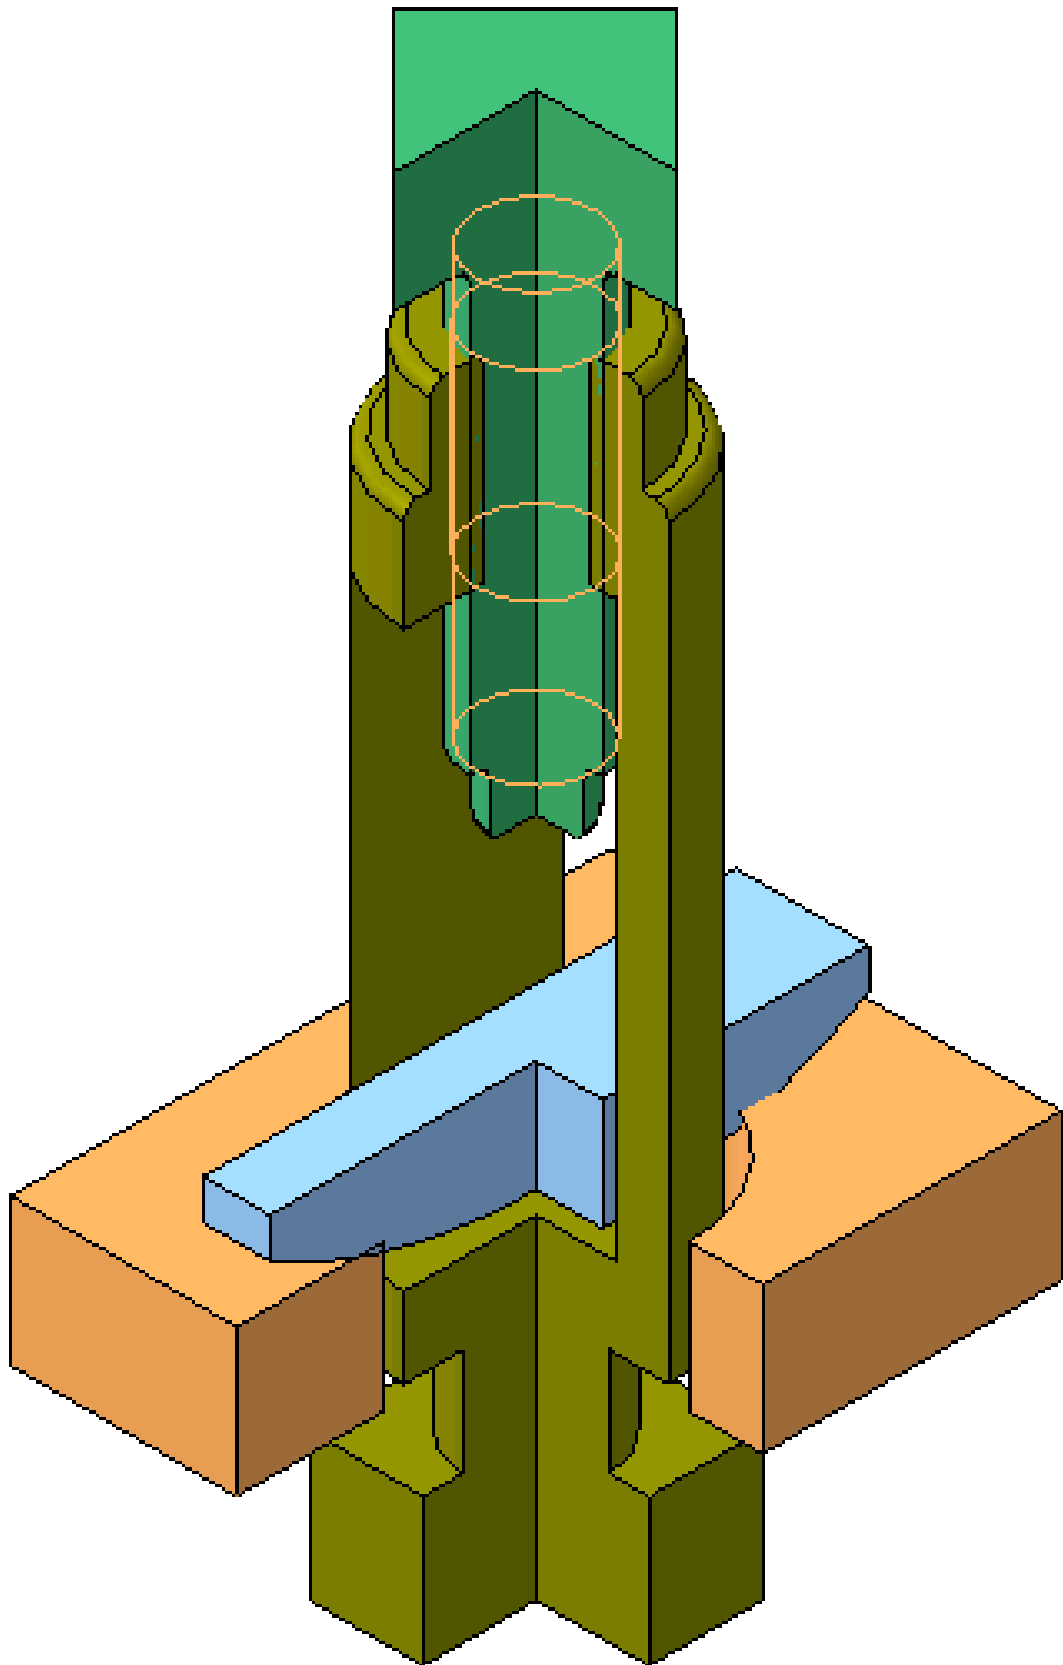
3D-модель сборки изделия «Резцедержатель» (варианты 15, 35)
